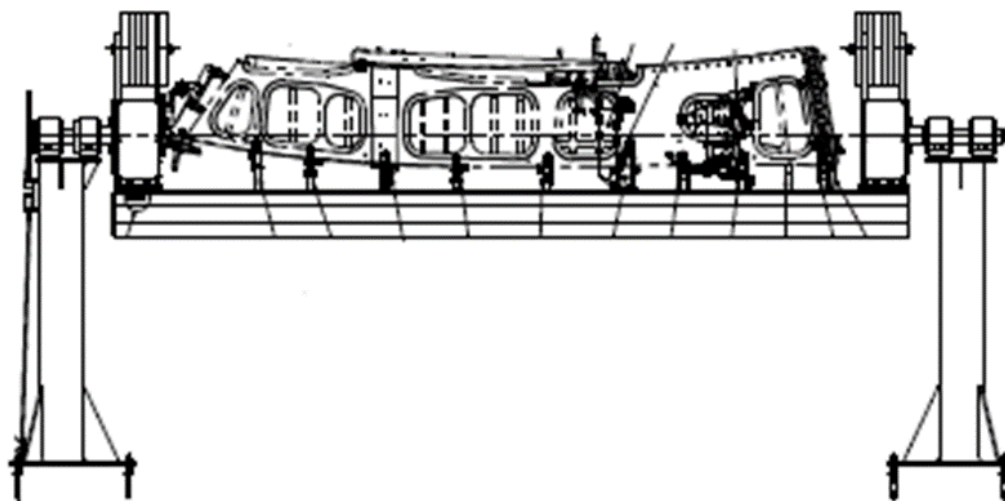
Estaleiro (JIG) de montagem do conjunto superior
